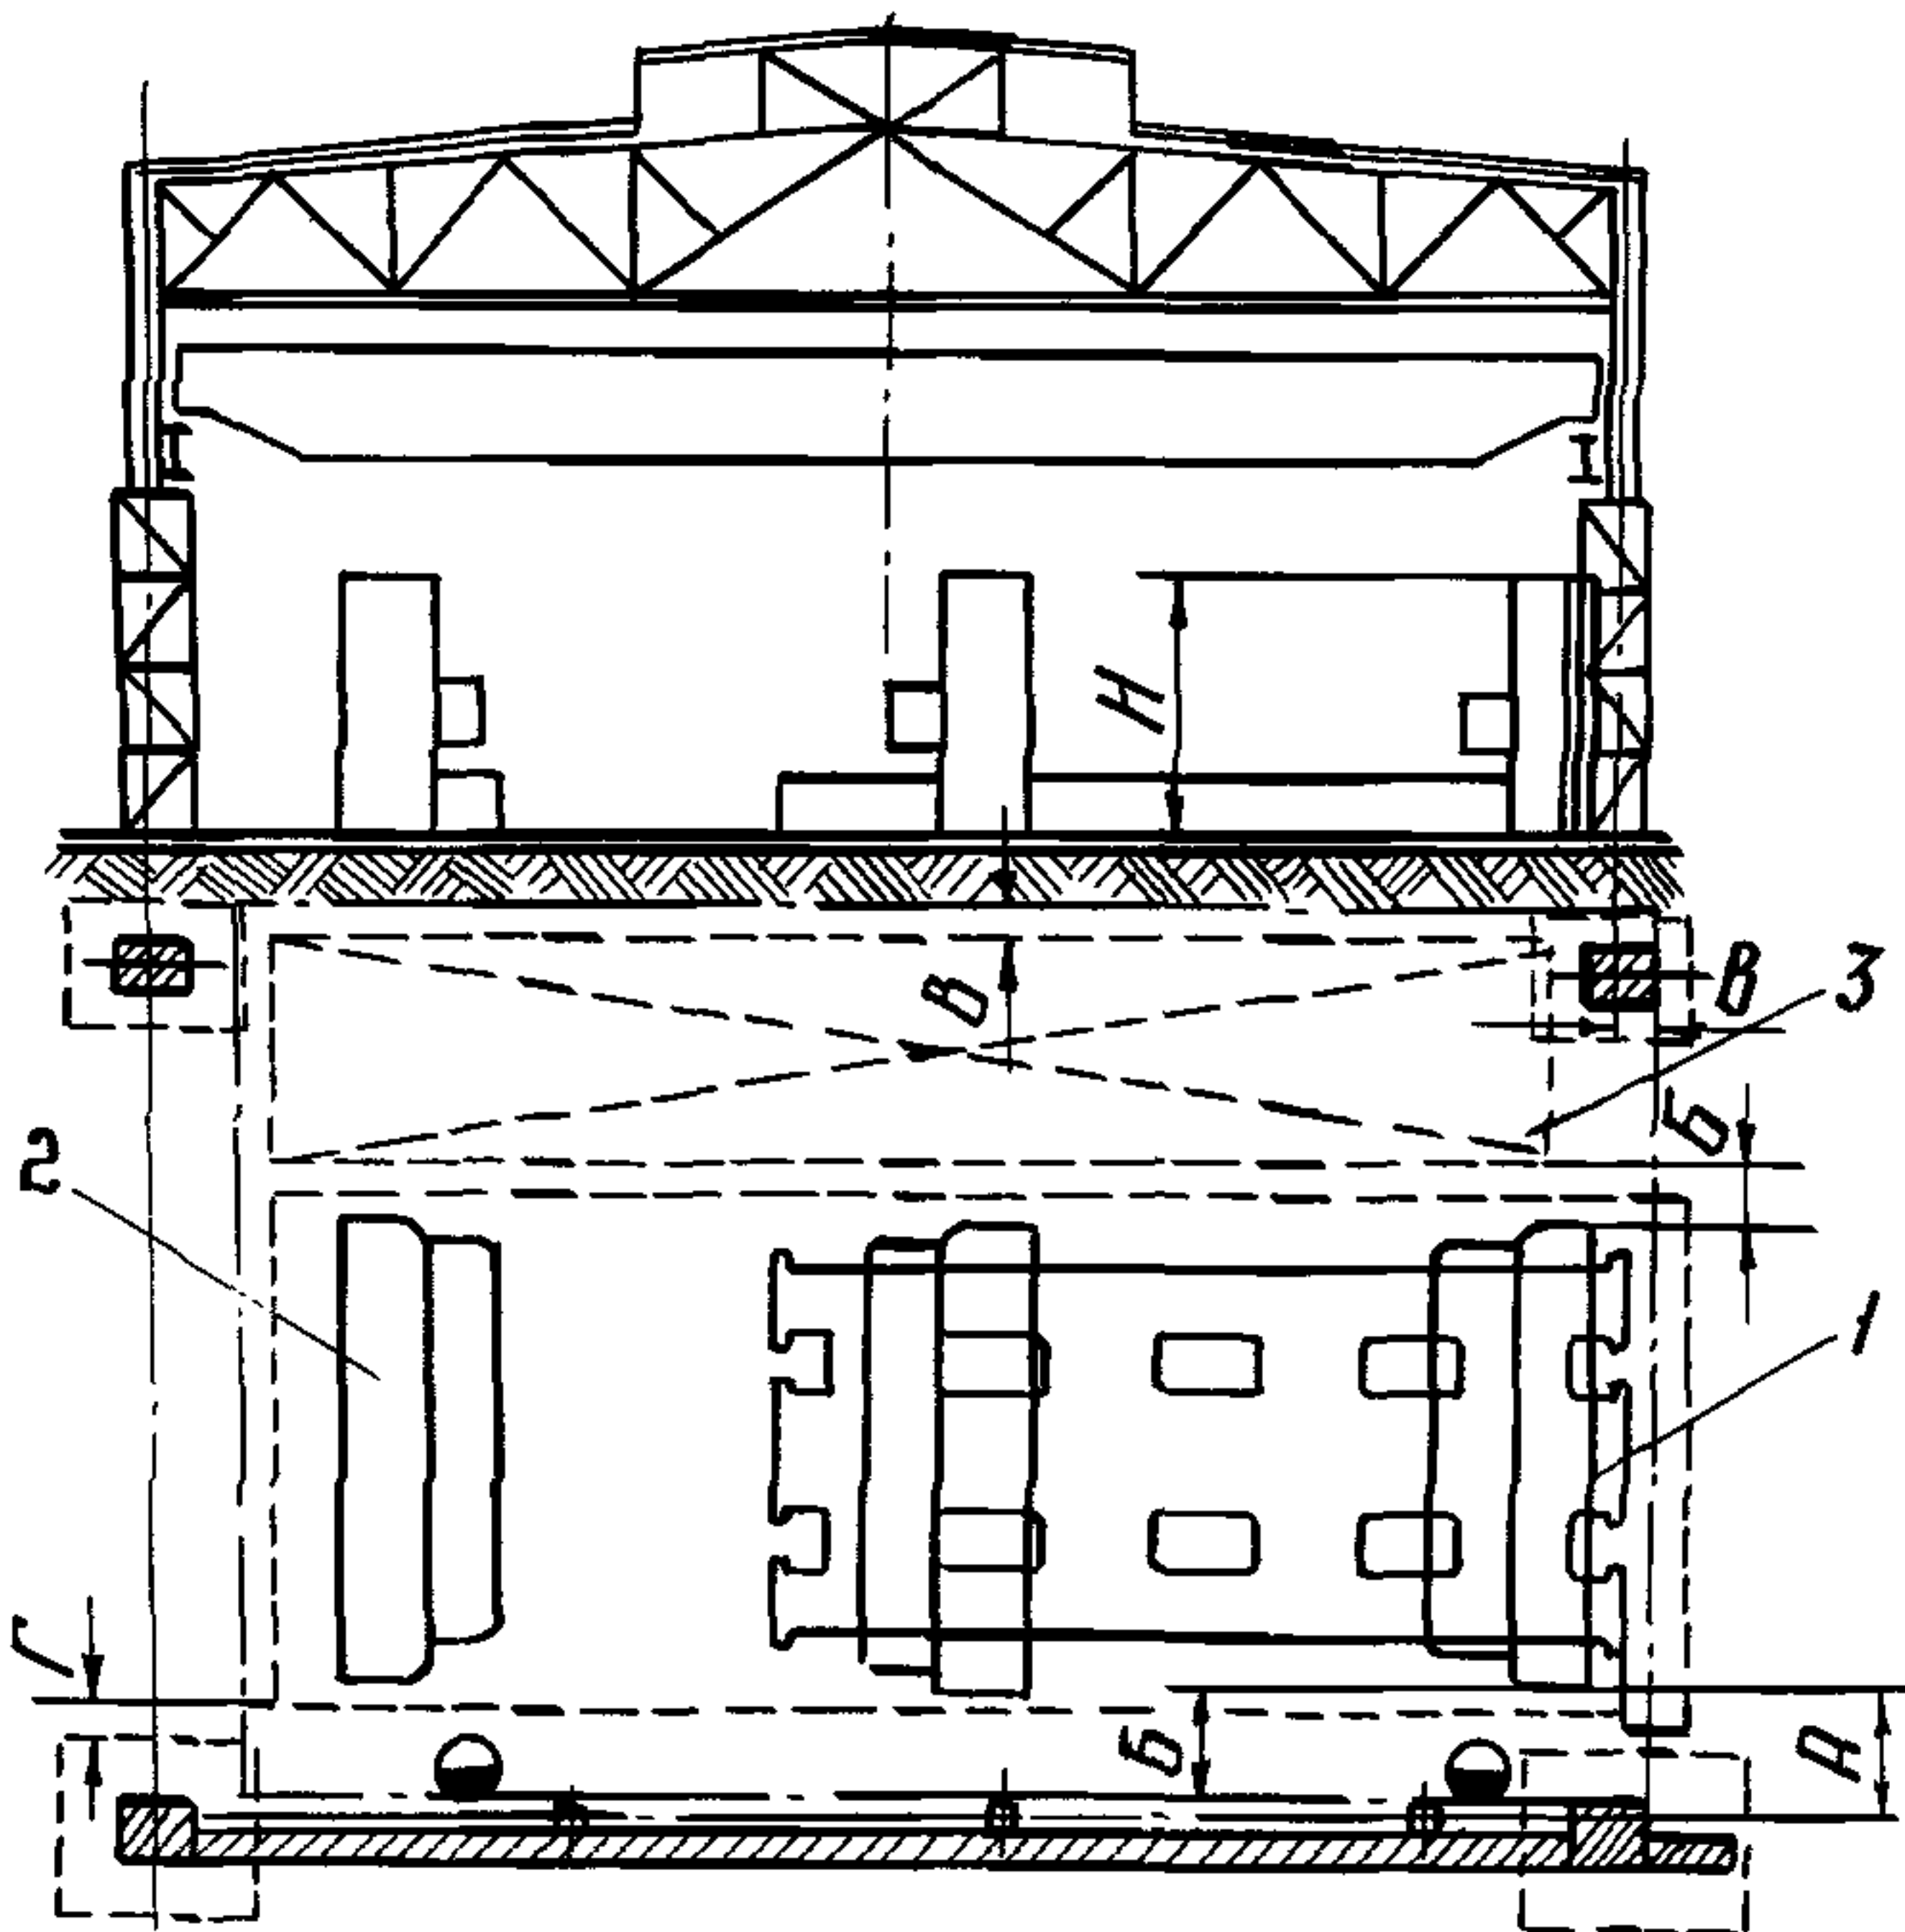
Размещение двухстороннего торцефрезерного станка в поперечном пролете:
